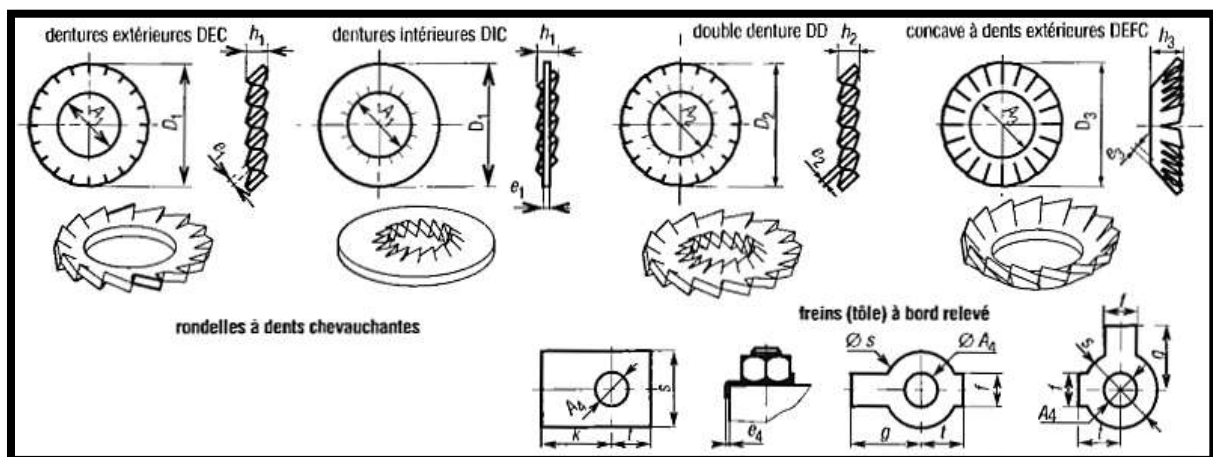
Dimensions des rondelles à dents chevauchantes et des freins à bord relevé
